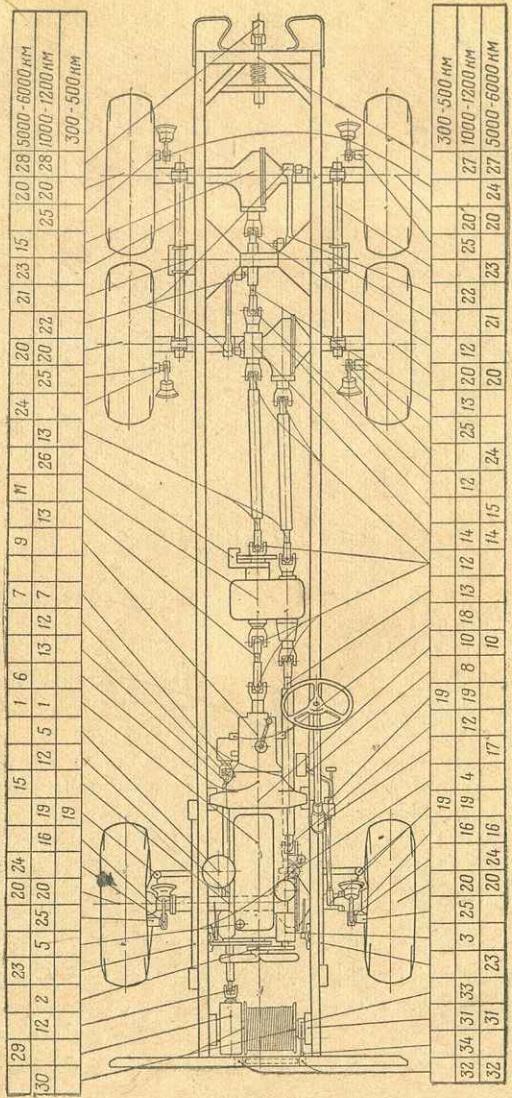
Схема смазки автомобиля ЗИЛ-157
